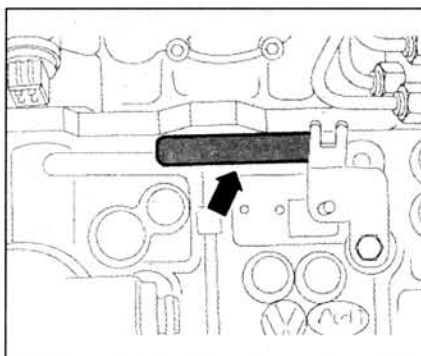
а. Расположение кода 5-цилиндровых двигателей.
